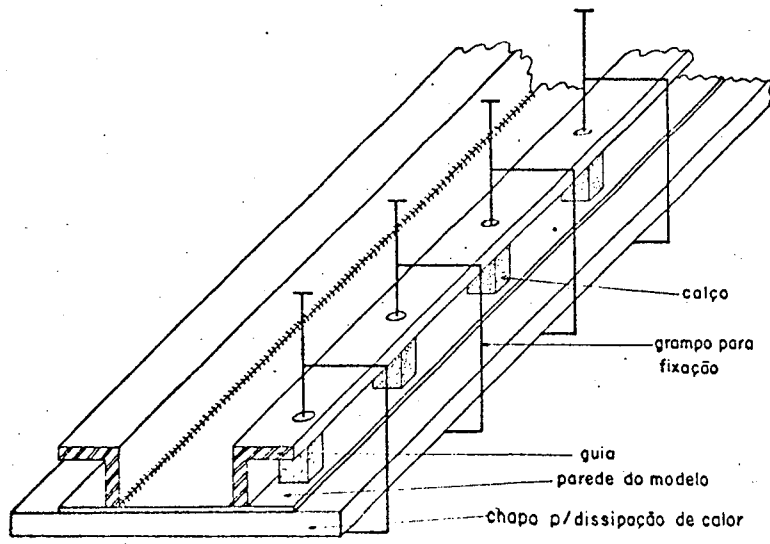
Aspecto do posicionamento das guias sobre o modelo para soldagem
